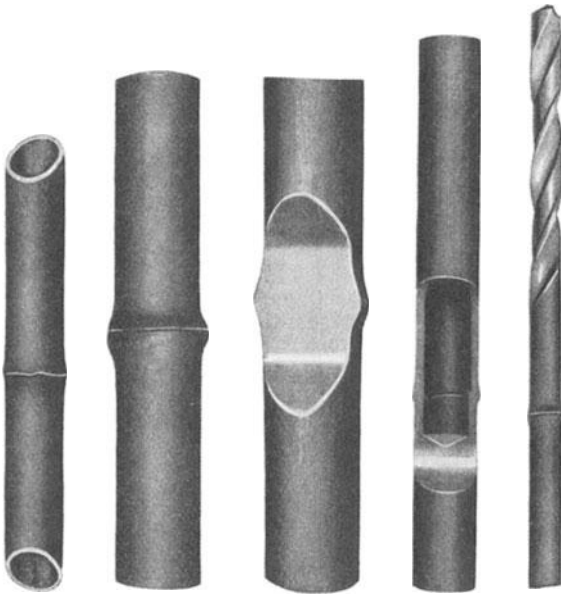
Stumpfgeschweißte Rohre und Rundeisen.
